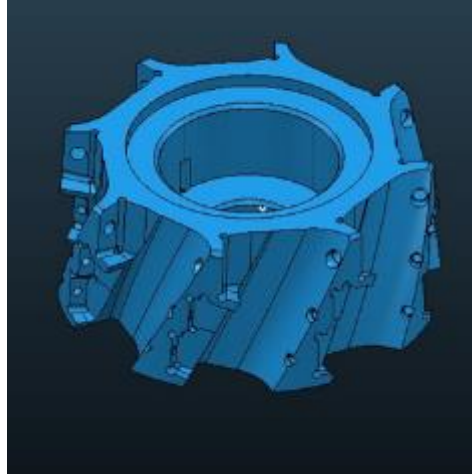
Модель корпусу РІ, імпортована в САМ – системі Powermill
